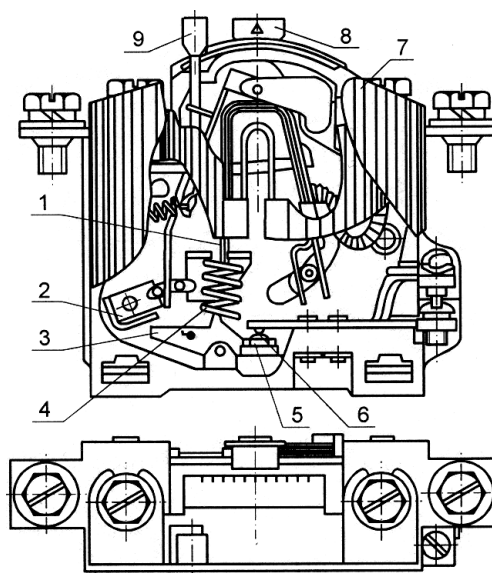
Тепловые реле типа ТРП: 1 — биметаллическая пластинка; 2 — упор самовозврата; 3 — держатель подвижного контакта; 4 — пружина; 5 — подвижный контакт; 6 — неподвижный контакт; 7 — сменный нагреватель; 8 — регулятор тока уставки; 9 — кнопка ручного возврата.
